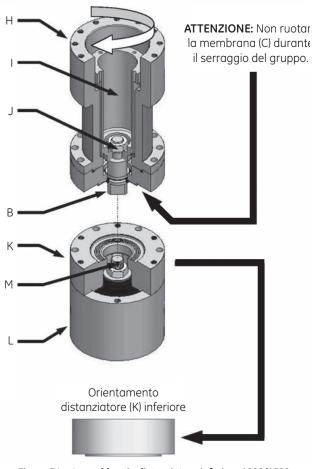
Assemblaggio distanziatore inferiore 1000/1500
